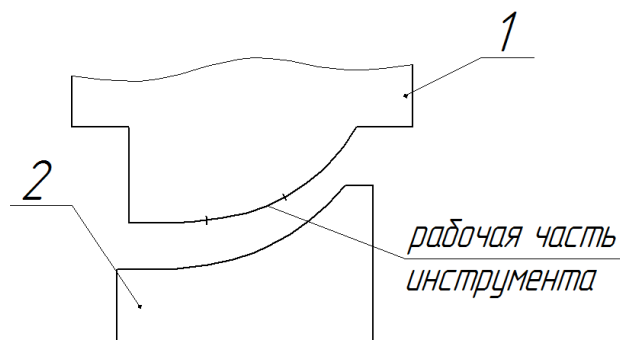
Гибочный штамп: 1 - верхний рабочий инструмент, 2 - нижний рабочий инструмент
